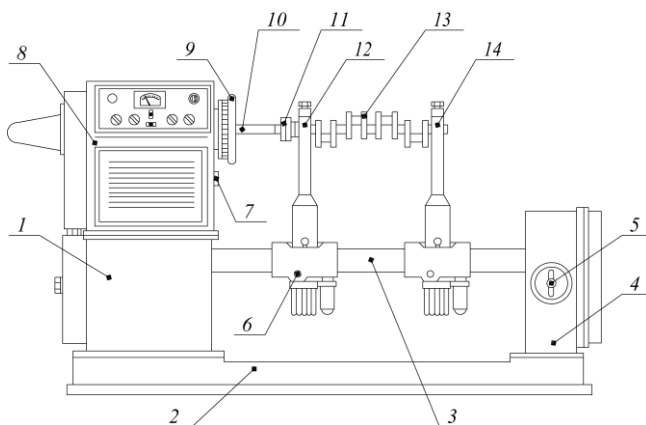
Общий вид балансировочного станка КИ-4274: 1, 4 – стойки; 2 – плита; 3 – трубчатые направляющие; 5 – пакетный выключатель; 6 – стопорный винт опоры; 7 – кнопка включения электродвигателя; 8 – шпиндельная бабка; 9 – маховик; 10 – приводной вал; 11 – соединительная муфта; 12, 14 – опоры; 13 – коленчатый вал
